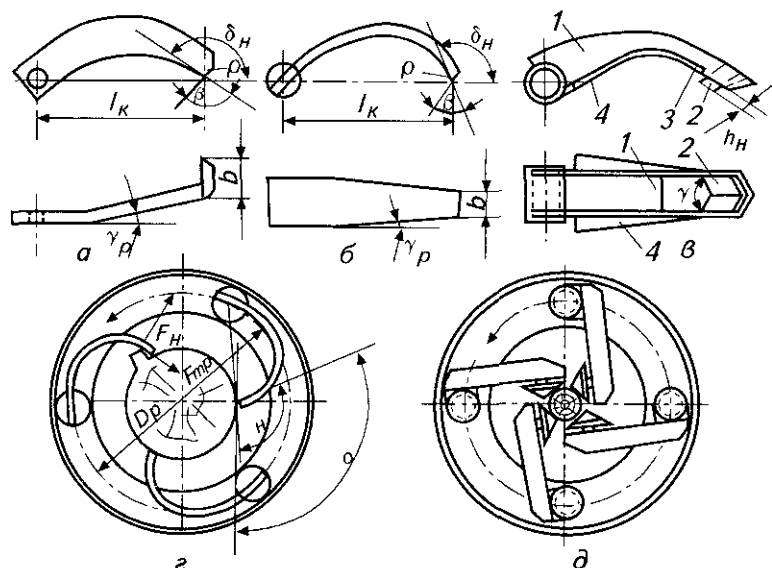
Окорочный инструмент роторных окорочных станков: а, б – скребковый окорочный инструмент; в – ножевой окорочный инструмент; г – схема взаимодействия короснимателя с остатками сучьев; д – схема установки конических фрез на роторе станка
